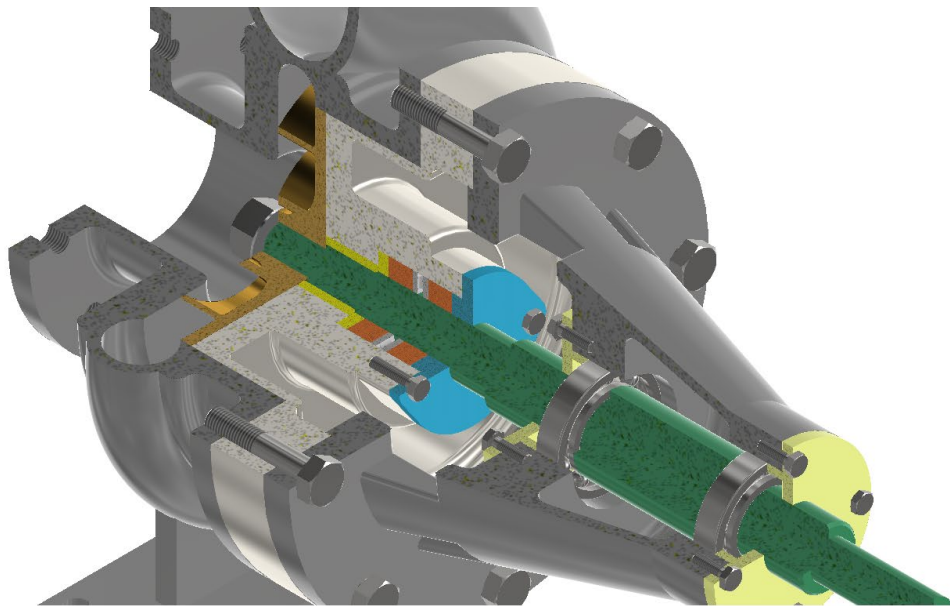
Bomba centrífuga ensamblada (seccionada con zoom)
